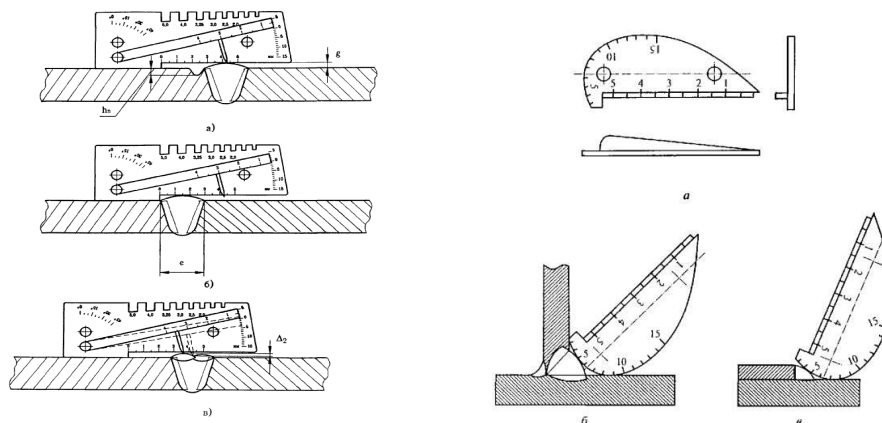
Способы измерения сварных швов с помощью шаблонов
